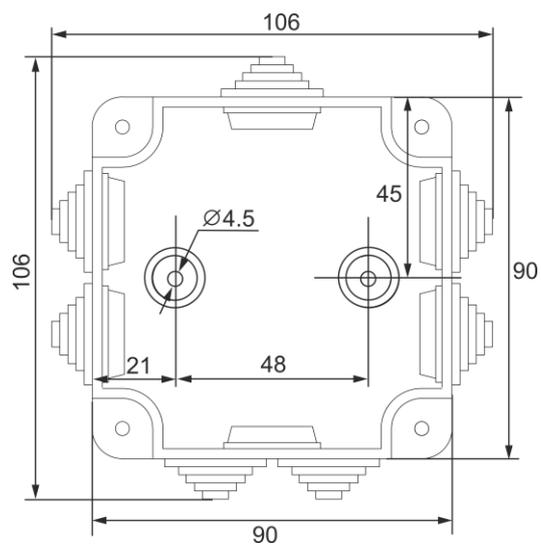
Установочный чертеж основания корпуса ПИУ-А24Б при применении совместно с двумя ПИУ-А24Р
